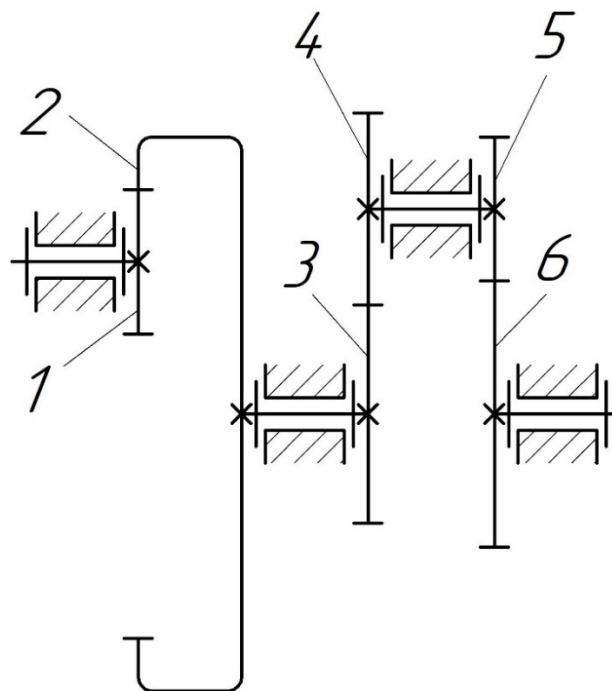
зубчатая передача с последовательным соединением зубчатых колес (ступенчатая)
